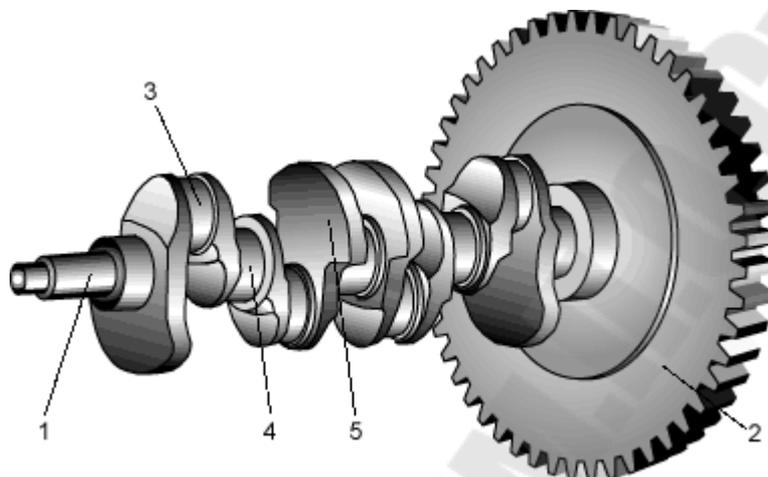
Коленчатый вал двигателя с маховиком
